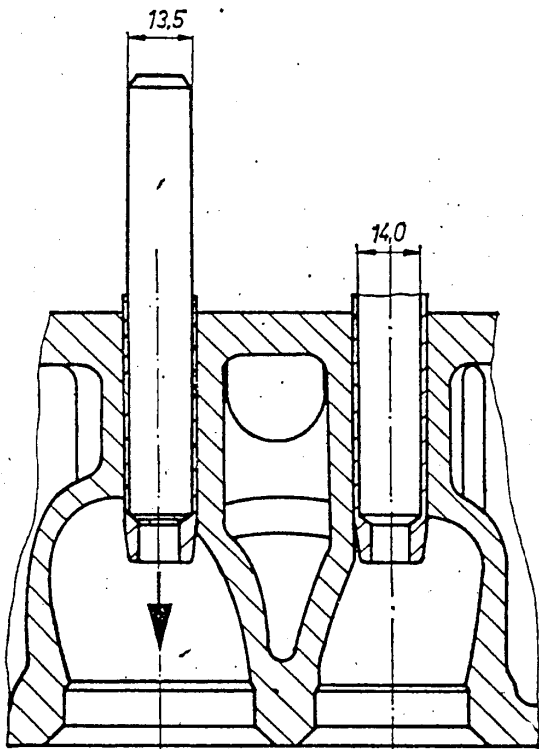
Ventilführungen aufbohren (14,0 mm)
